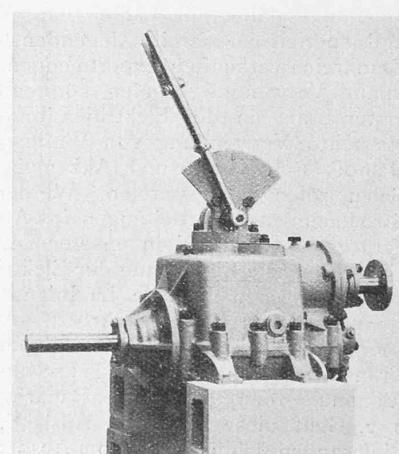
Flüssigkeits-Wechsel- und Wende-Getriebe, System Heinrich Schneider, für Werkzeugmaschinen- u. Hebezeug-Antriebe, gebaut von der Schweizer. Lokomotivfabrik Winterthur.
